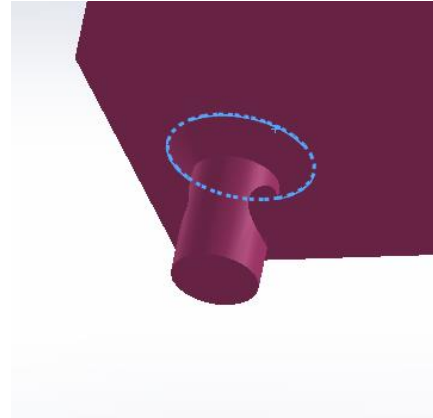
Vista de soldado de pieza N°13 (Fuente 101)
